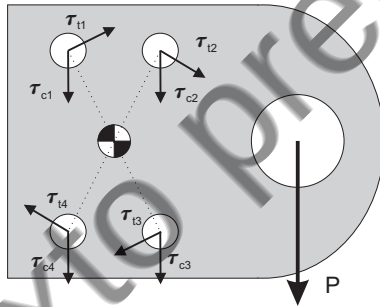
Tensão cisalhante na junta devido ao carregamento excêntrico.
